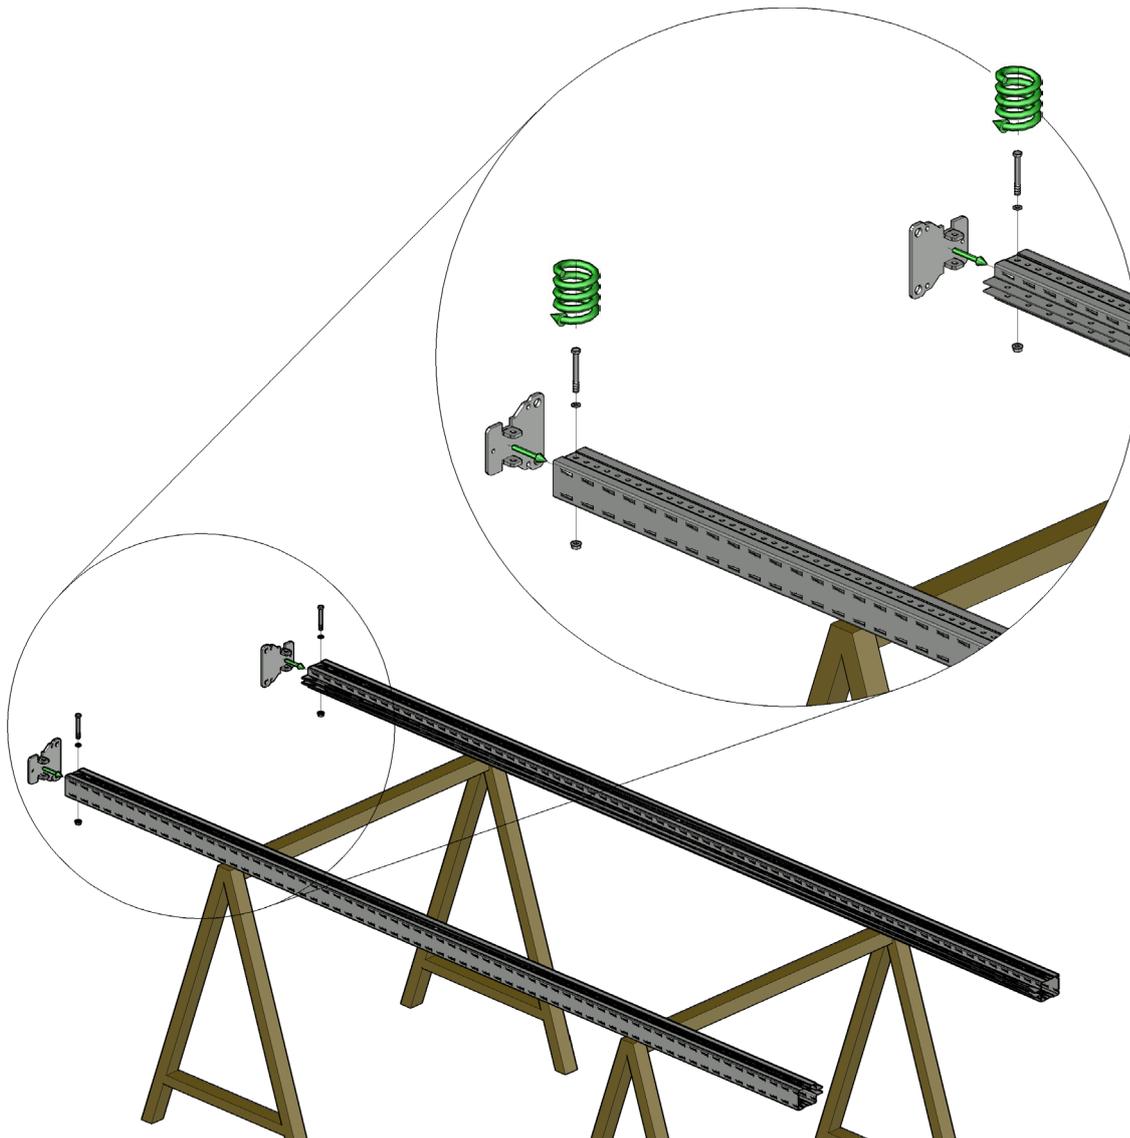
Montage der Fußplatten mit Schrauben, Federringen und Muttern
